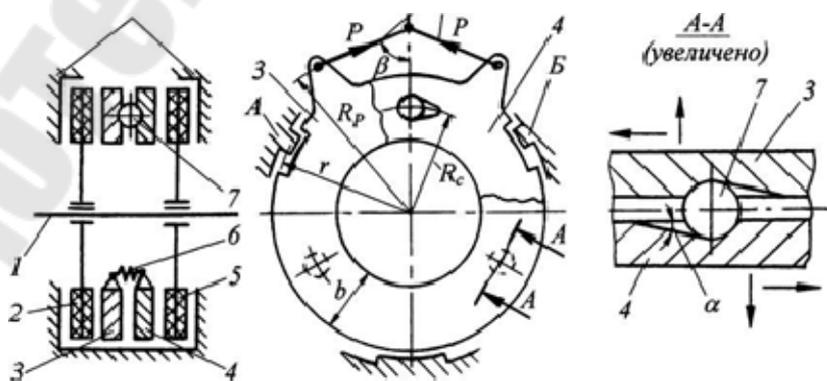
Схема закрытого дискового тормоза с сервоусилением.
